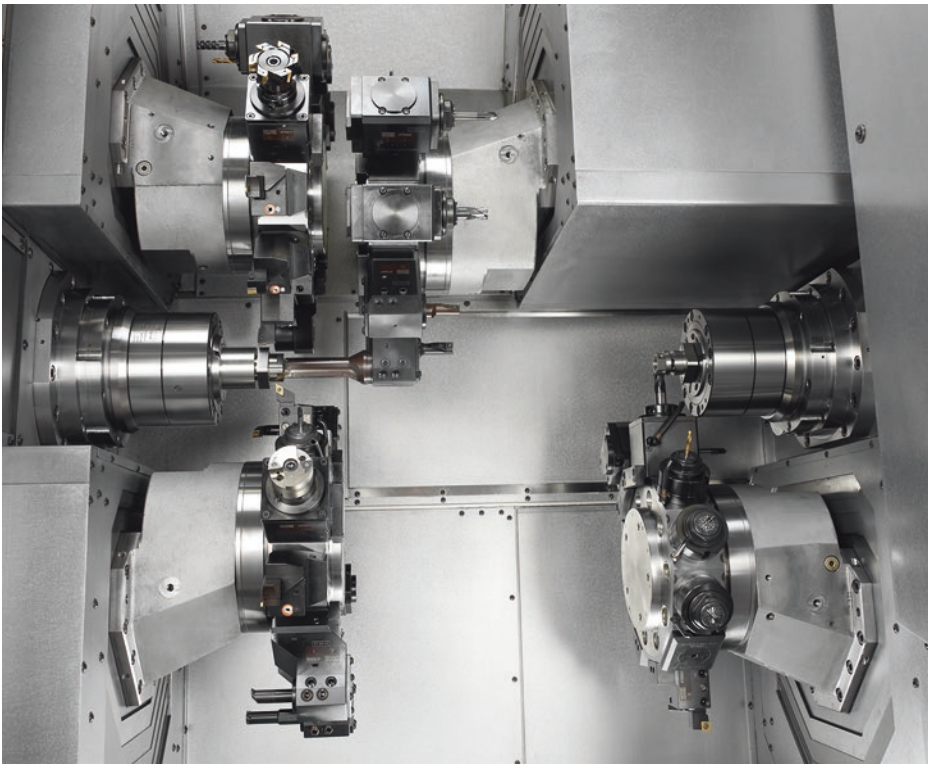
Beispiel für eine CNC-Dreh-Fräsmaschine mit vier Werkzeugrevolvern, Haupt- und Gegenspindel [Trau16]
